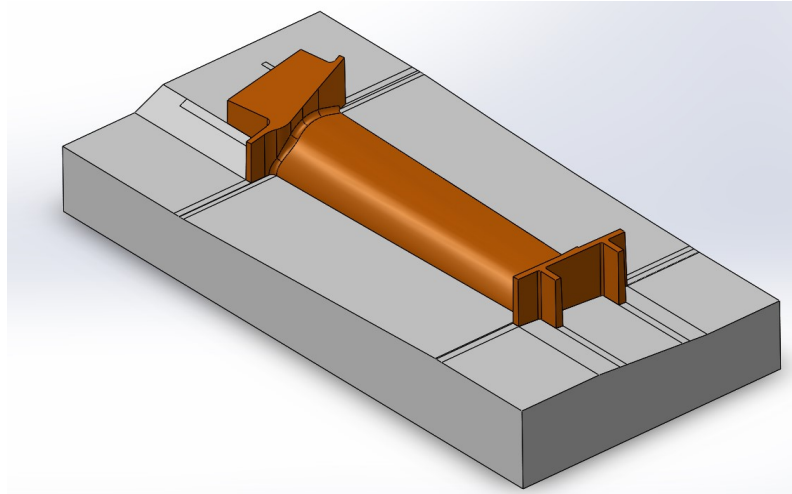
"Cama" destinada ao fabrico de molde em resina
